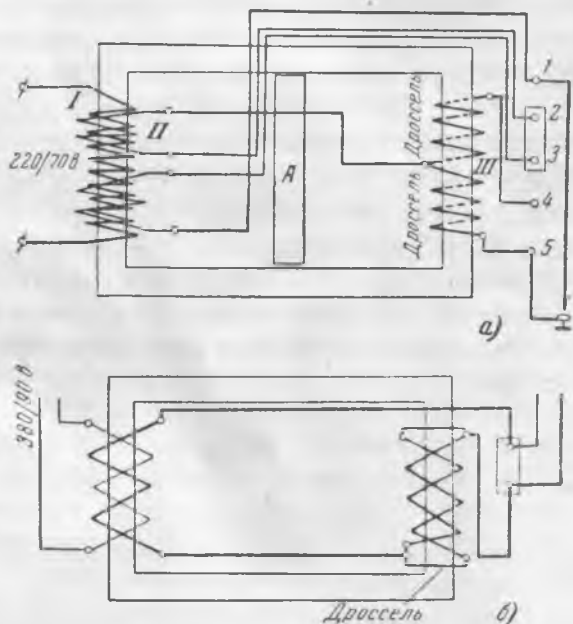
Принципиальная схема сварочного трансформатора СТАН-1-Ш.
